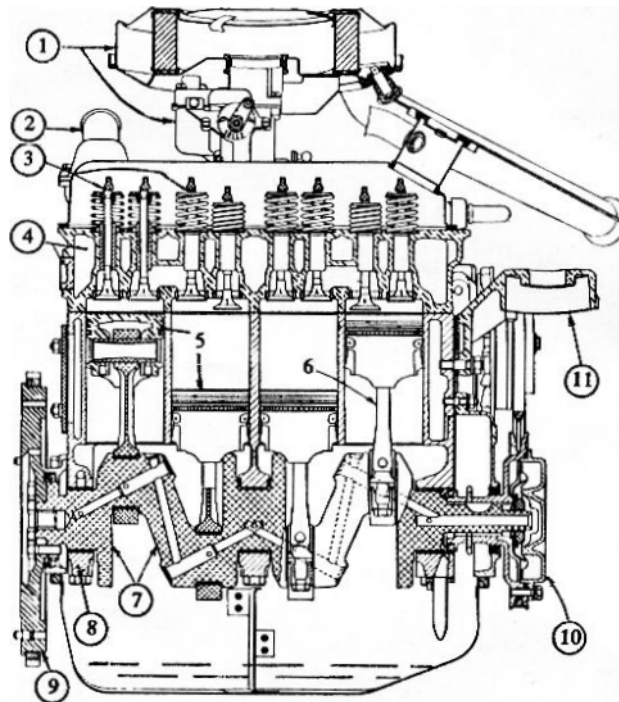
Corte longitudinal del Motor Fiat 850.
